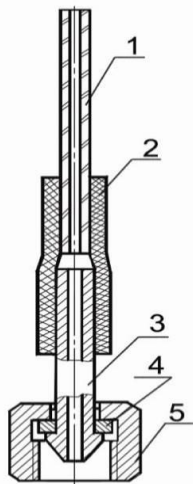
Моментоскоп: 1 – стеклянная трубка; 2 – резиновая переходная трубка; 3 – отрезок трубки высокого давления; 4 – шайба; 5 – гайка
